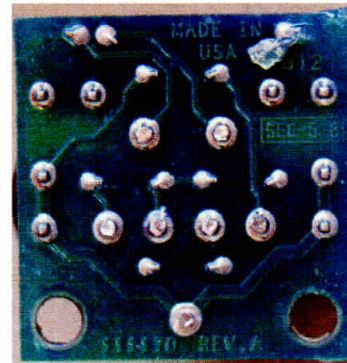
Tarjetas Handle Switch identificada con número de parte 111171 REV B, vista cara de soldaduras.
